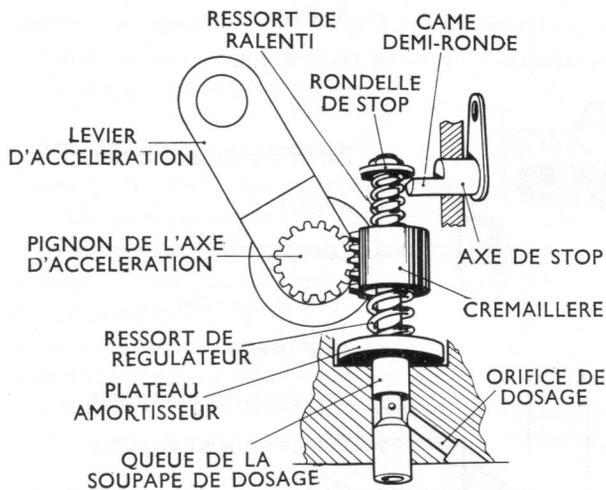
Soupape de dosage et axe de stop d'un régulateur hydraulique à pignon et crémaillère
